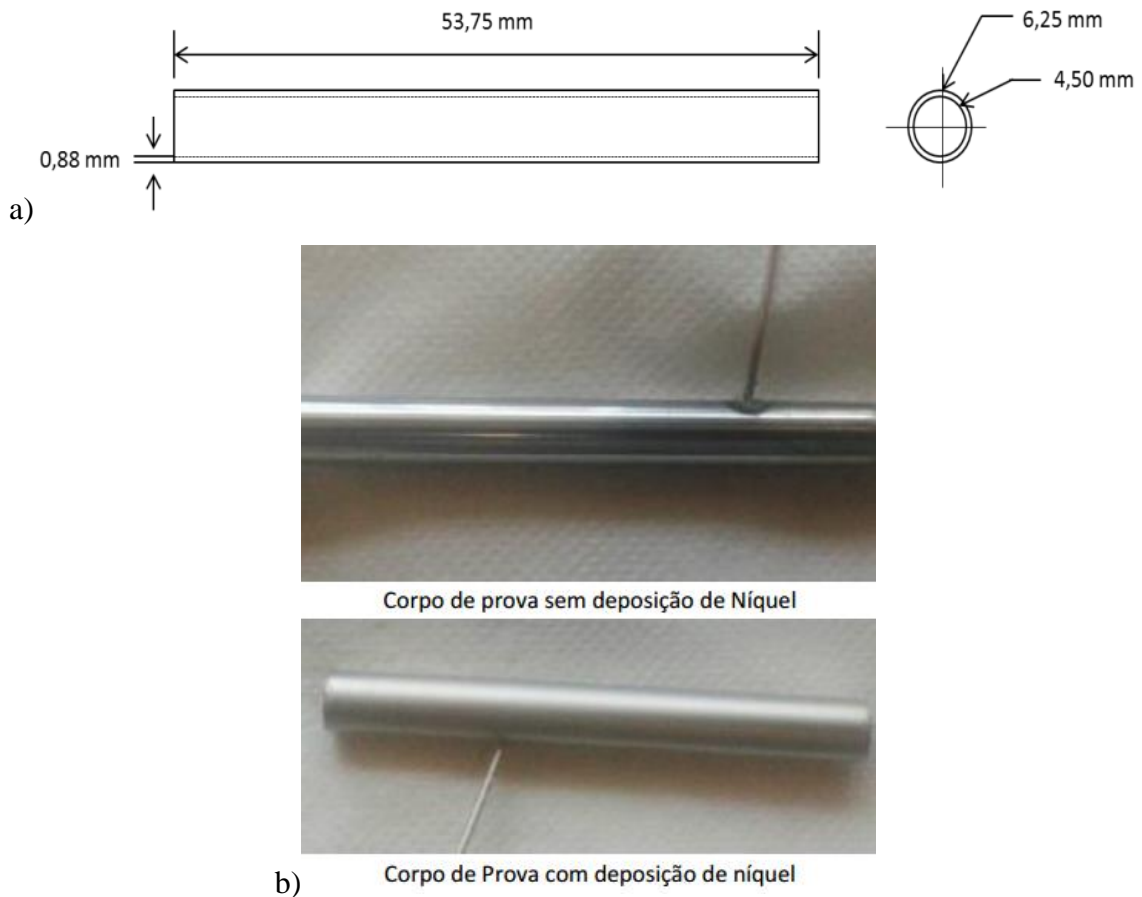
Corpo de prova: a) Desenho técnico; b) fotos.
